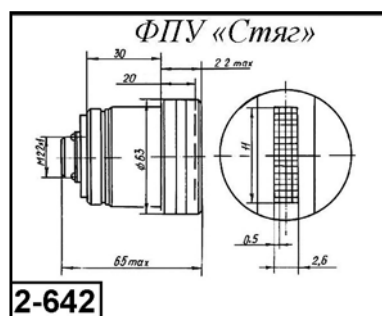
Внешний вид и габаритные размеры ФПУ «Стяг»
